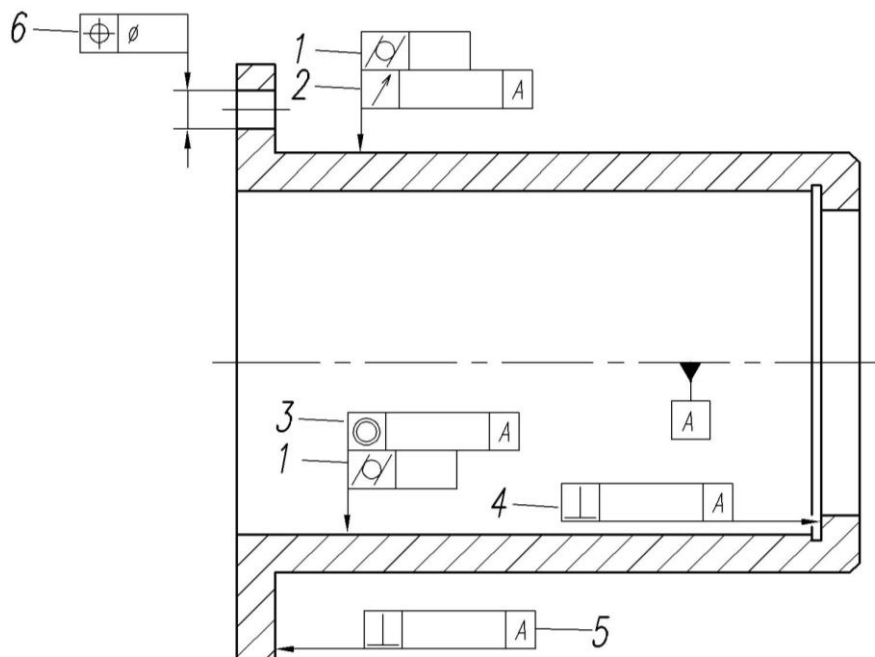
Размещение обозначений допусков форм и расположения поверхностей на чертеже стакана
